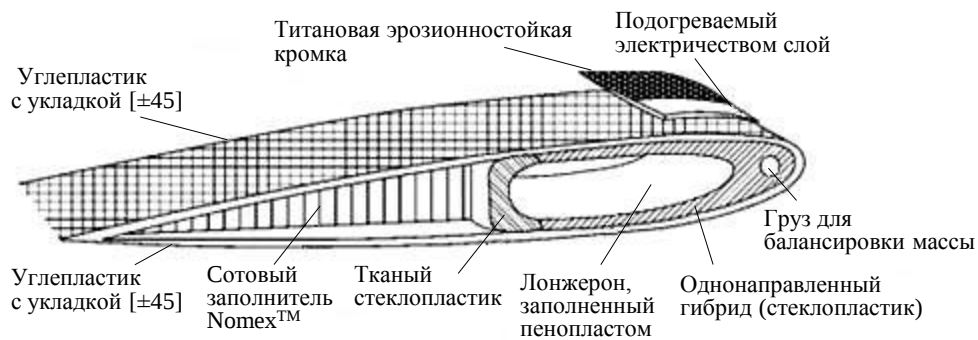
Типовой вариант конструкции лопасти несущего винта вертолета
